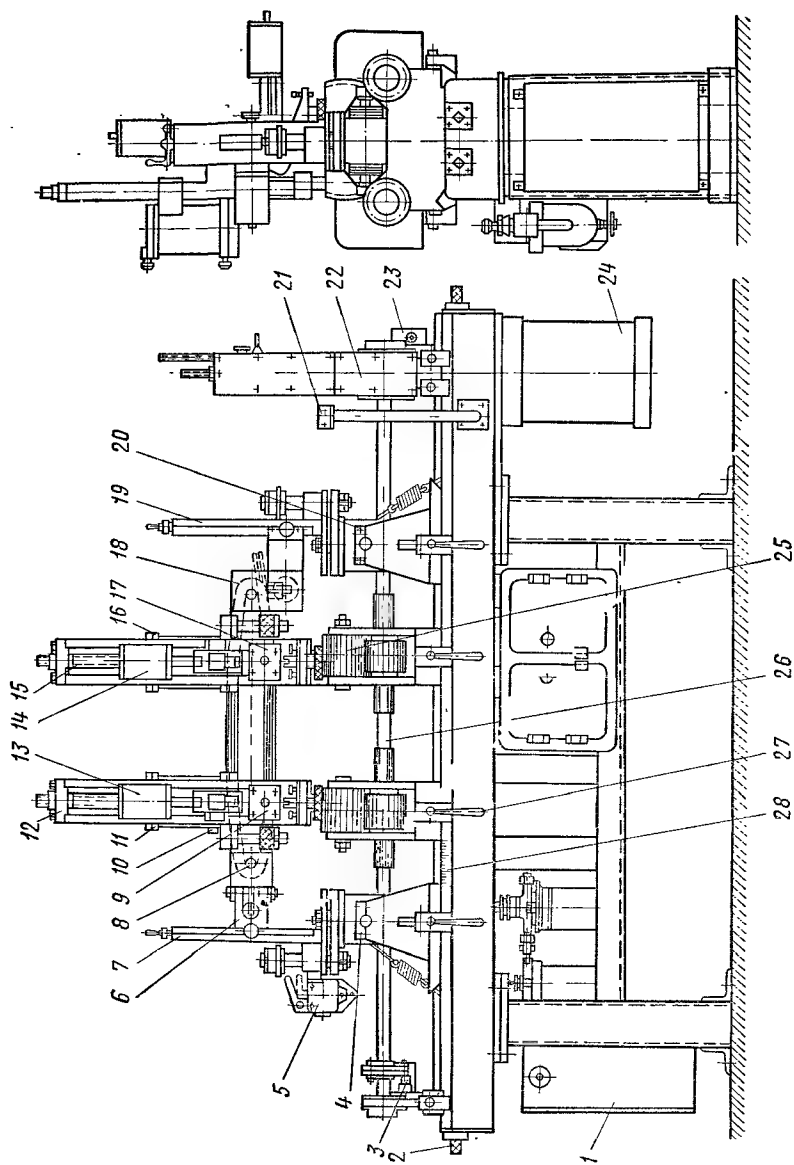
Полуавтомат для растяжки и формовки катушек статора
